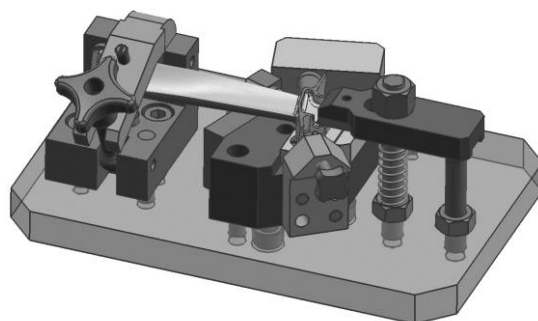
Пример станочного приспособления для обработки лопаток турбины
